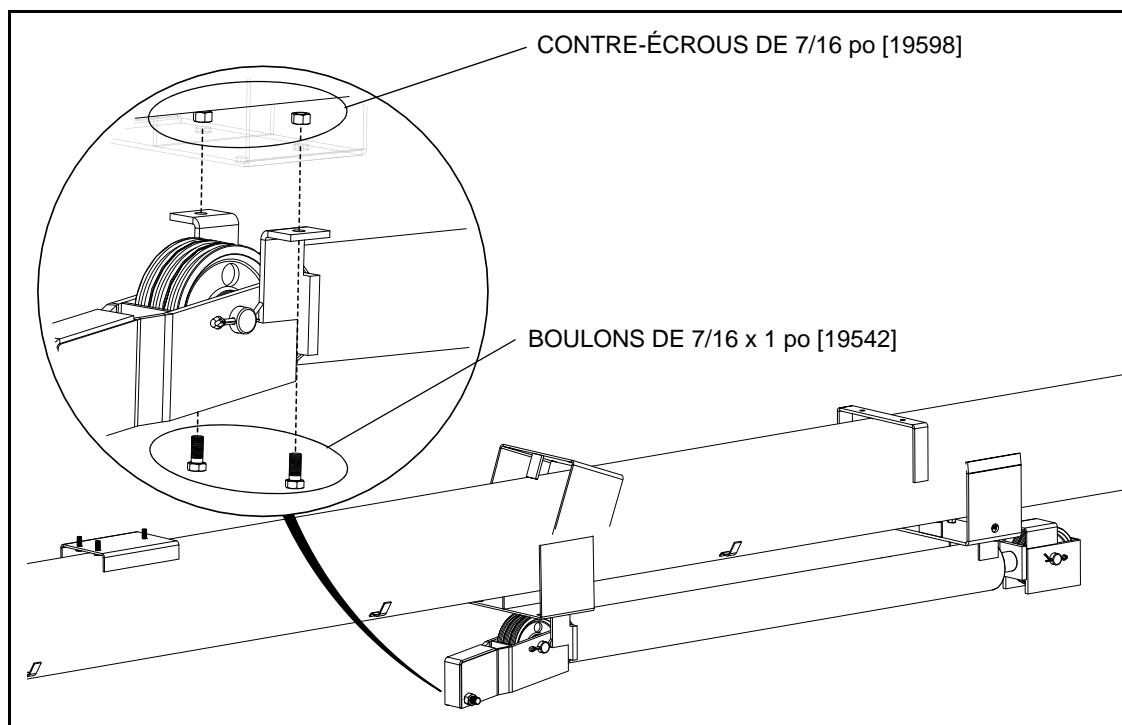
Installation du cylindre de levage (MKX100-53/63/73)
